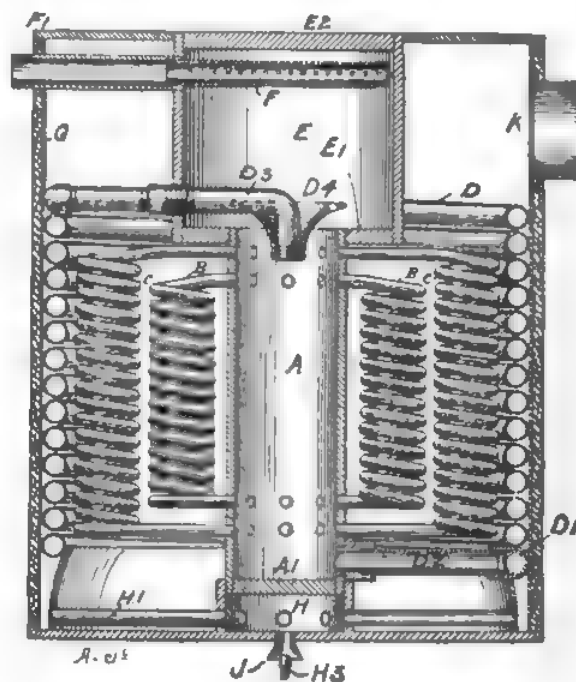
Schnitt durch Kessel, Spiralrohre in Ansicht.
